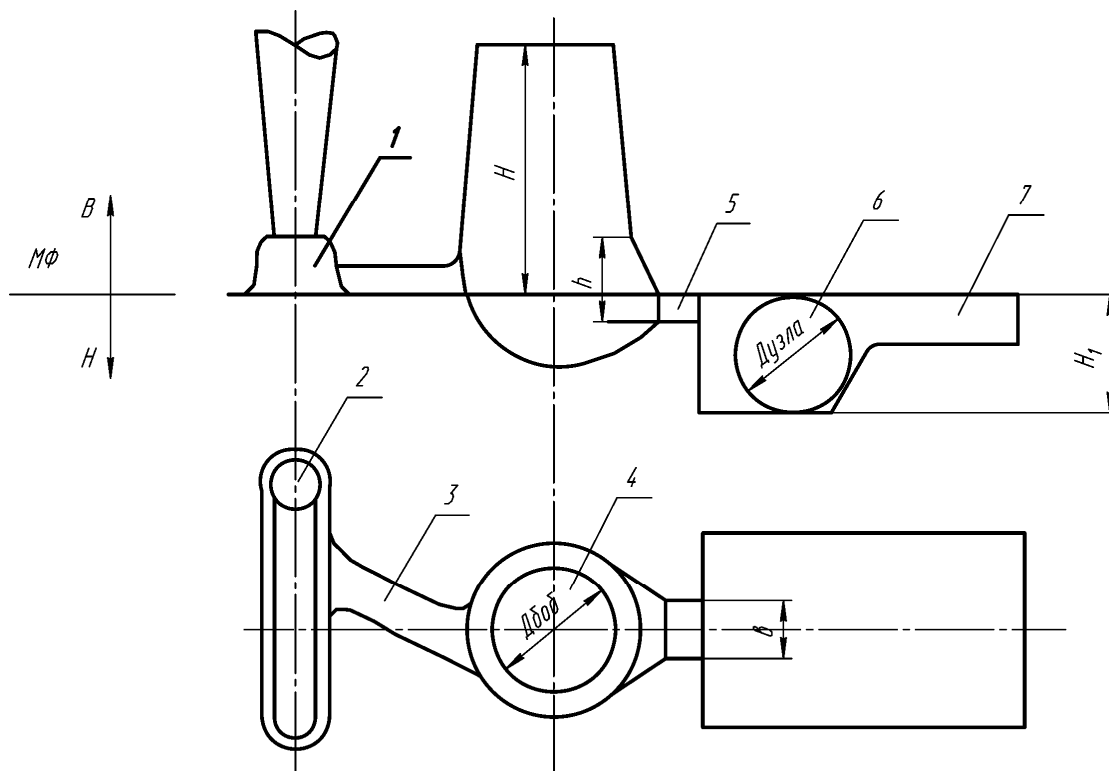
Эскиз питающей бобышки и подвод металла:
